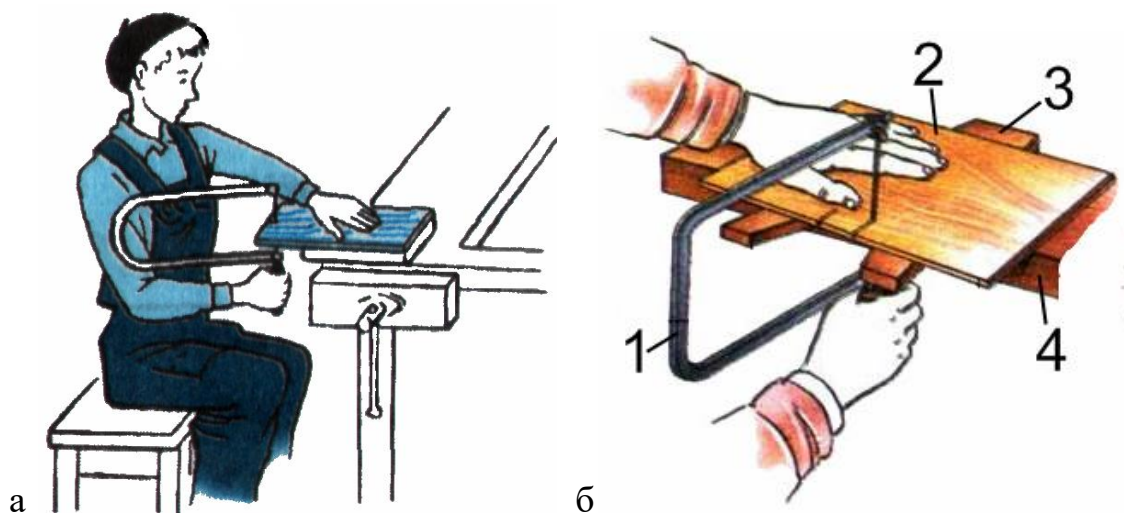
Учебное место: а – рабочее положение; б – хватка лобзика: 1 – лобзик, 2 – заготовка, 3 – столик выпилочный, 4 – верстак.
